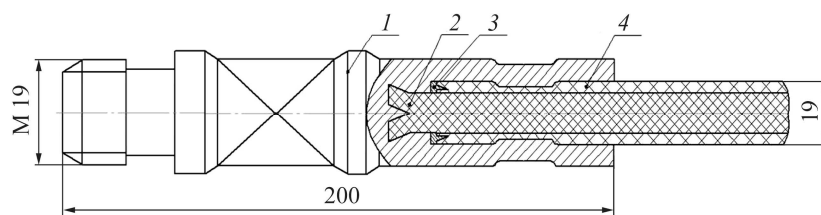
Конструктивне рішення з'єднання сталеві головки і полімерно-композитної частини гібридної штанги: 1 – сталеві головка; 2 – вуглепластиковий стрижень; 3 – розтискальне кільце; 4 – склопластикові оболонка.
